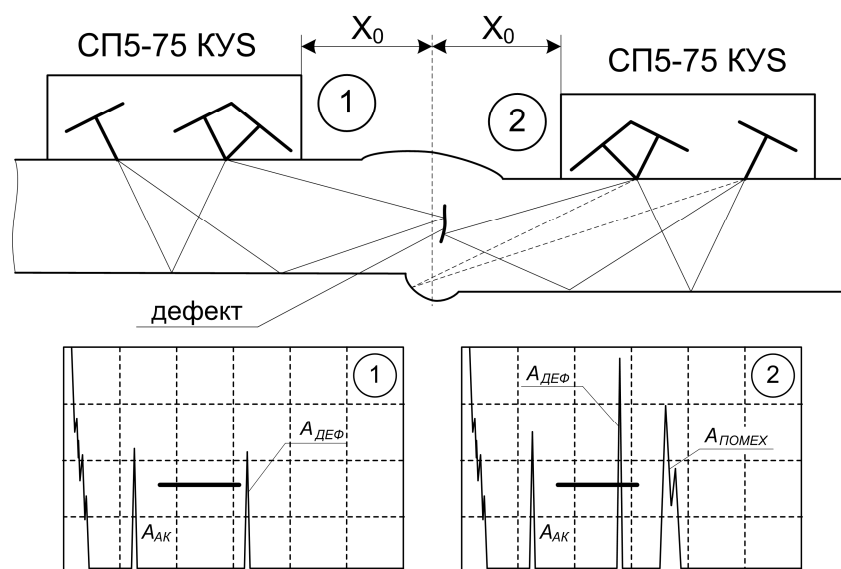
УЗК дефектного стыкового сварного соединений со смещением кромок.
